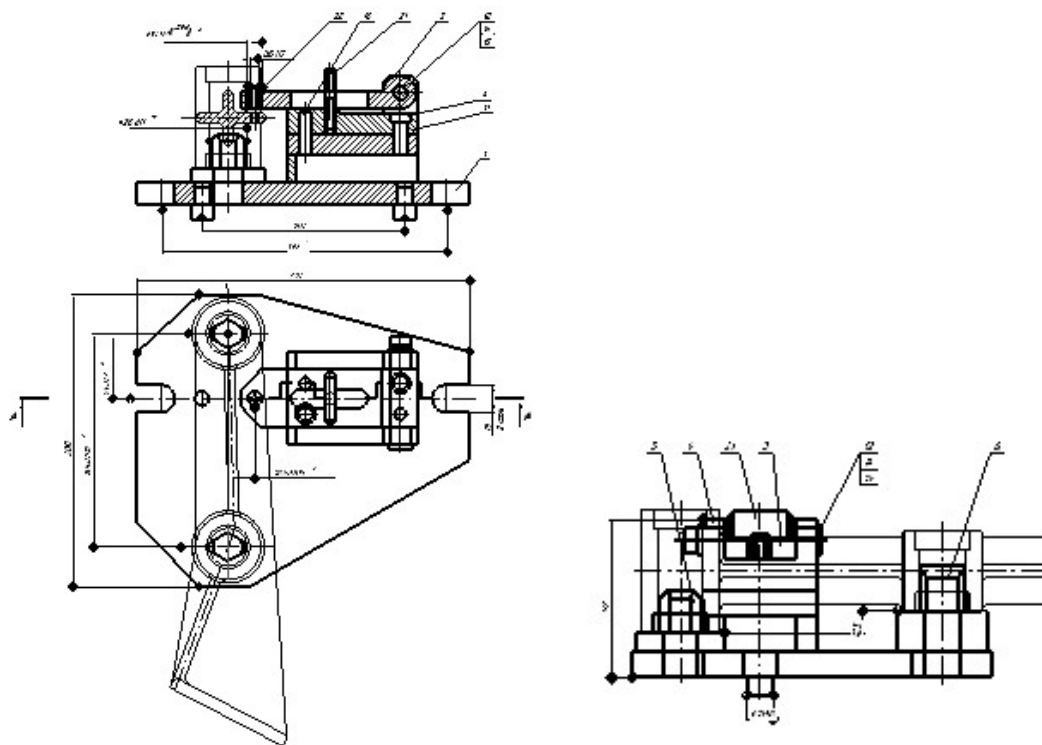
Схема базування та закріплення деталі при вимірюванні
